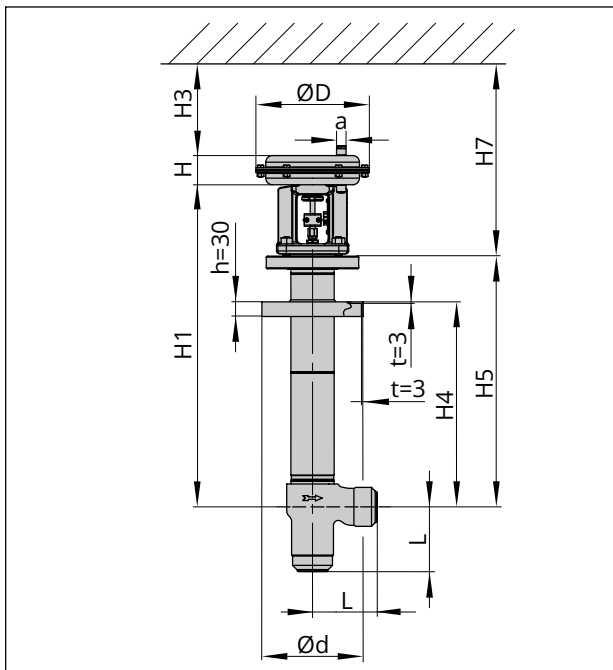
Eckventil Typ 3248-1 mit Edelstahlgehäuse
